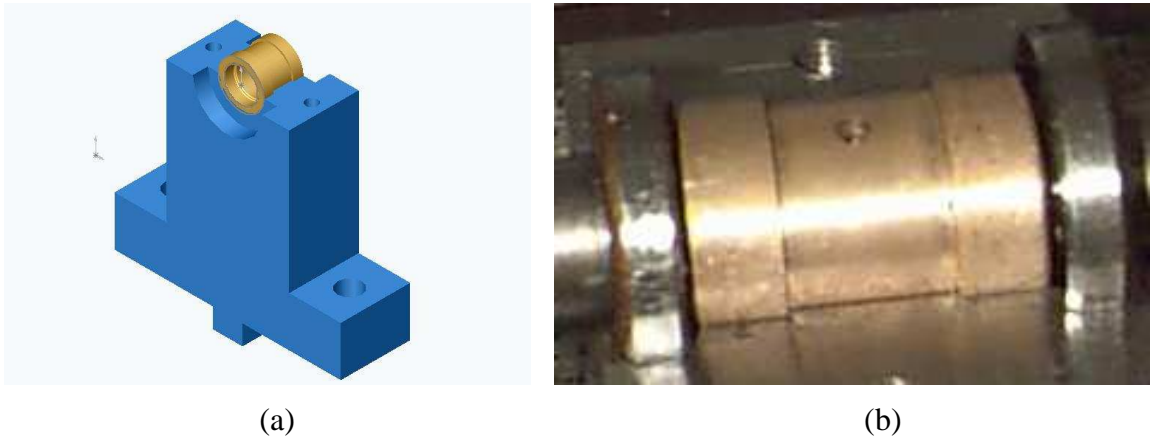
(a) Conjunto Mancal / Pedestal e (b) Mancal fabricado.
